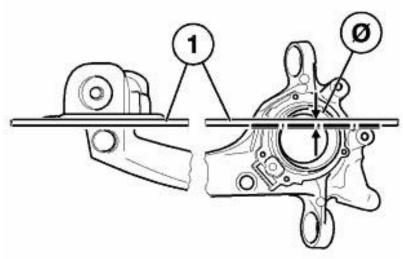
Längslenker ab 1998 mit einem Gewindeloch
